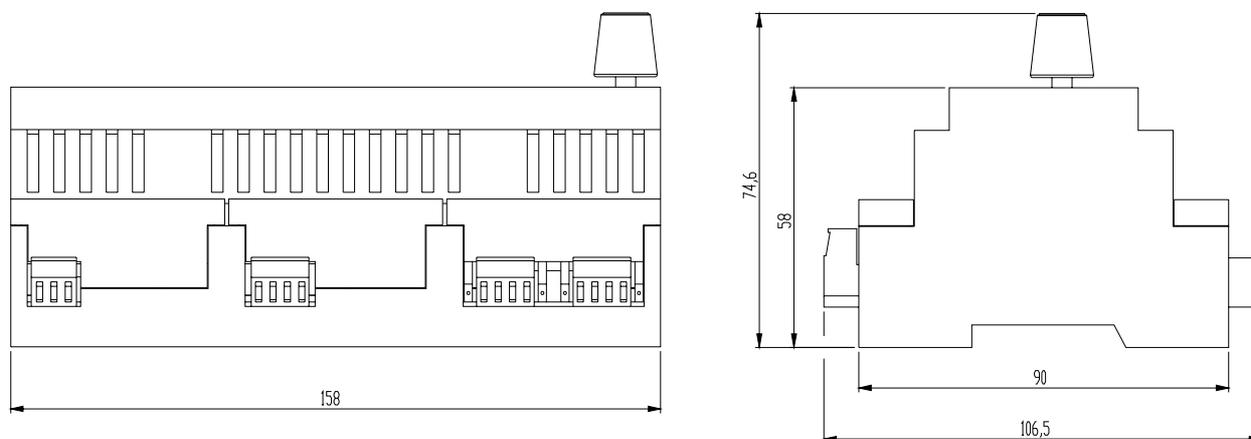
Dimensioni serie Robur Box: vista frontale e laterale
